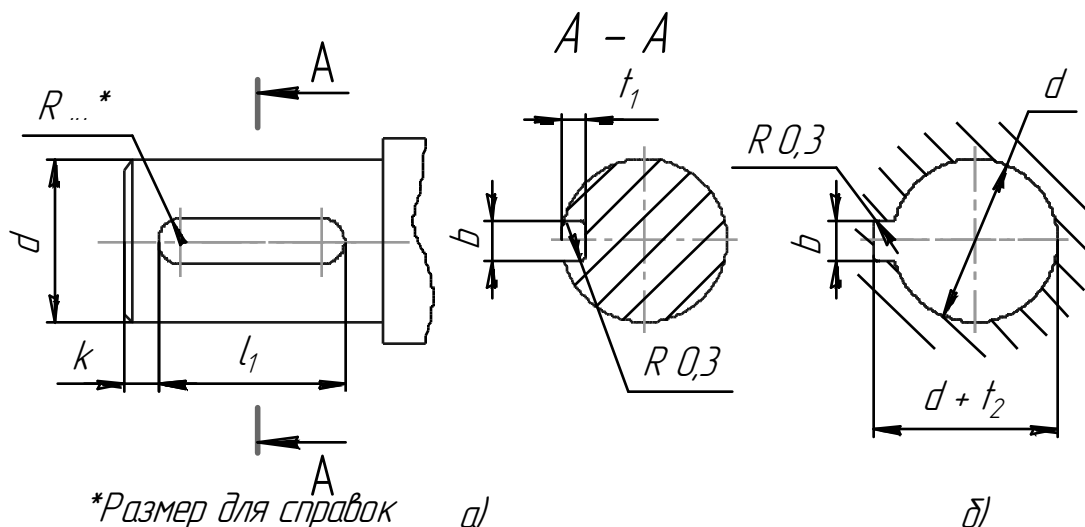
Размеры, наносимые на чертежах соединений призматическими шпонками
